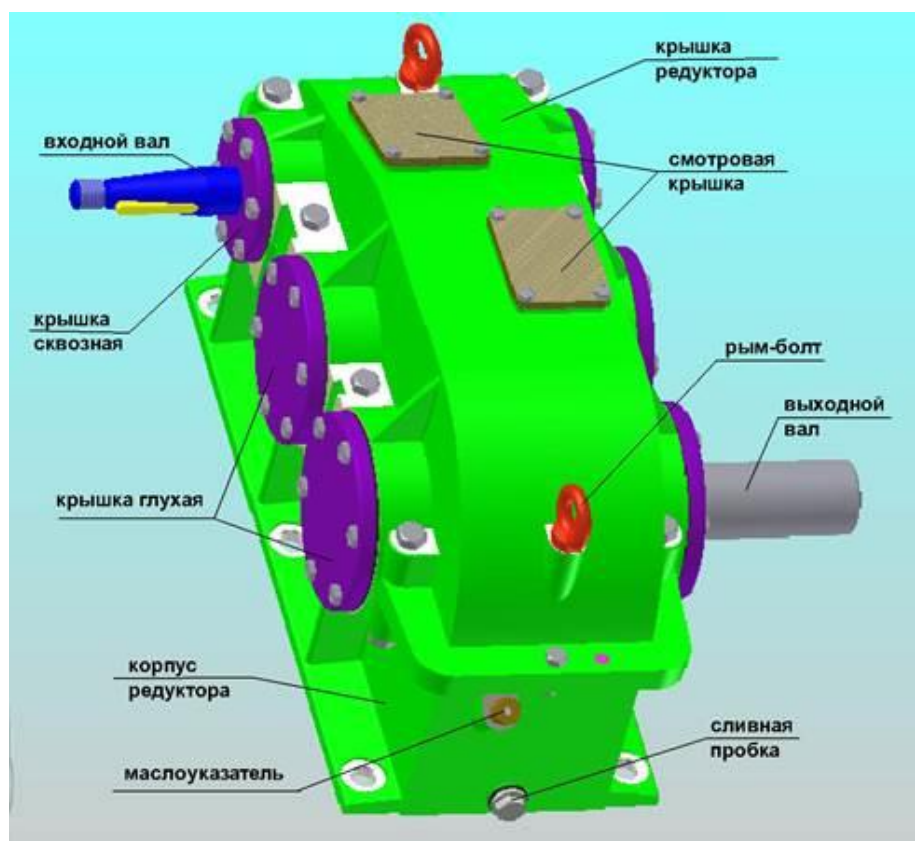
Редуктор зубчатый цилиндрический двухступенчатый
